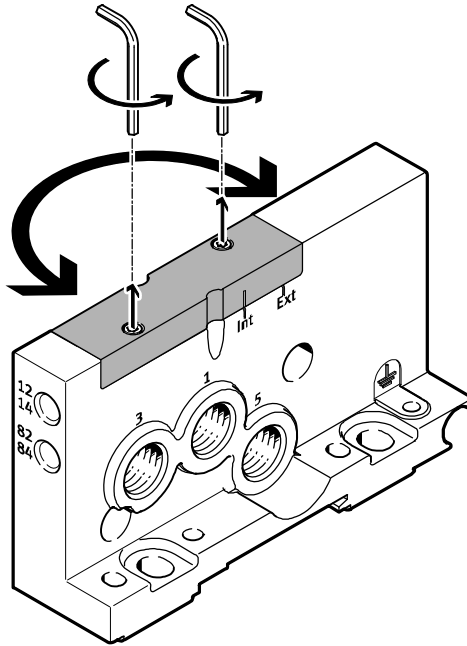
Umbau bei rechter Endplatte mit Versorgungsanschlüssen
